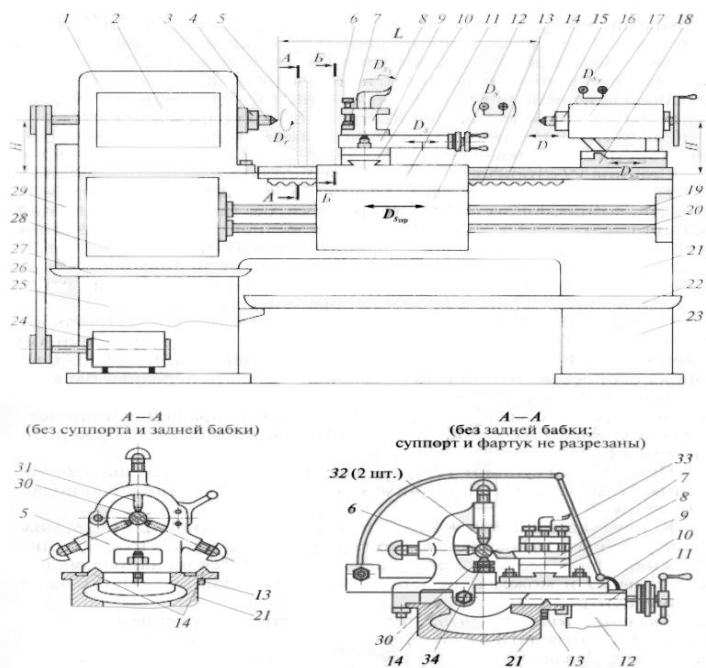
7. Общий вид универсального токарно - винторезного станка: 1 - передняя тумба; 2 - панель коробки скоростей, 3 - шпиндель, 4, 15 - центры, 5 - неподвижный лонет, 6 - подвижный лонет, 7 - резец, 8 - резцодержатель, 9 - верхний суппорт, 10 - поперечная каретка, 11 - продольный суппорт, 12 - фартук, 13 - зубчатая рейка, 14 - призматические направляющие, 16 - пиноль, 17 - корпус задней бабки, 18 - нижняя плита задней бабки, 19 - ходовой винт, 20 - ходовой валик, 21 - станина; 22, 27 - корыта, 23 - задняя тумба, 24 - электродвигатель, 25 - передняя тумба, 26 - ременная передача (условно отодвинута от станины, 28 - коробка подачи; 29 - коробка сменных зубчатых колес, скоростей; 30 - заготовка, 31 - упоры неподвижного лонета, 32, 34 - упоры подвижного лонета, 33 - защитный экран, D_v установочные движения элементов станка 8, 16, 17, 18
